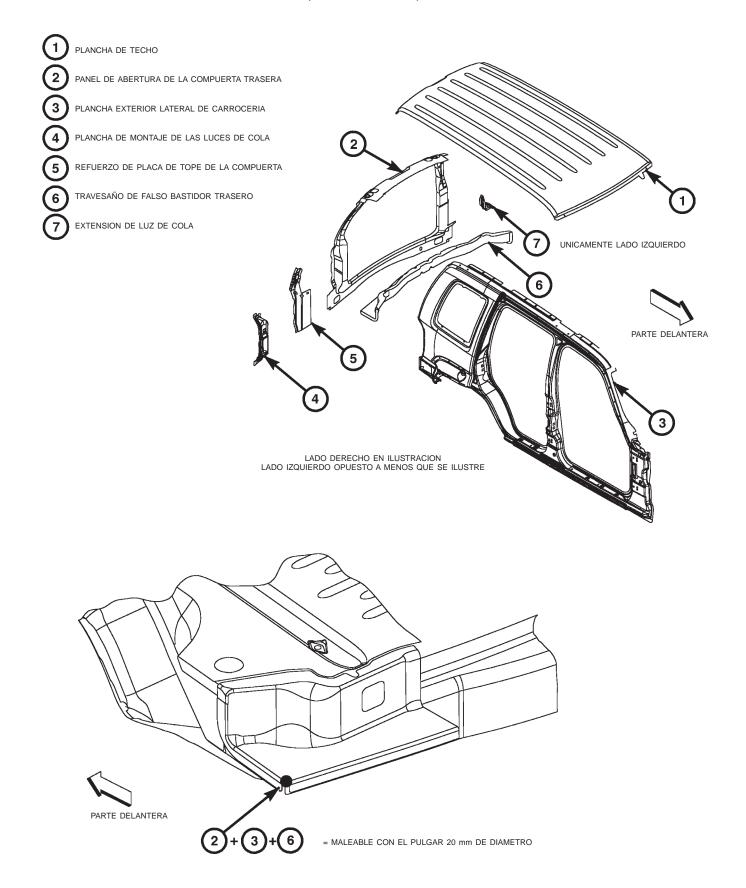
PLANCHA DE TECHO Y CONJUNTO DE VIGA LATERAL DE CARROCERIA
